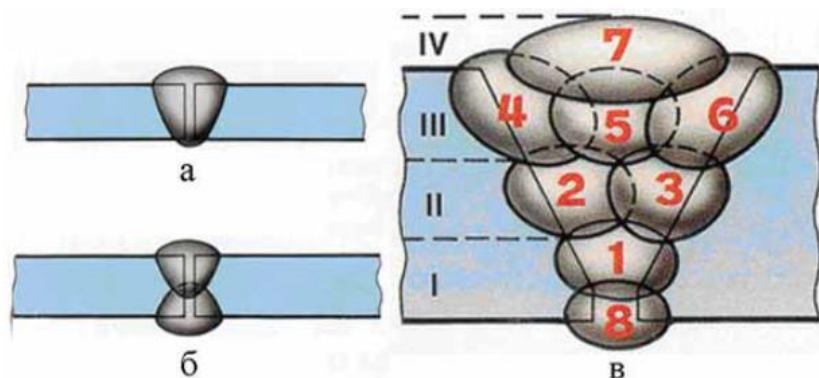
Одно-(а) и двухсторонний (б) односторонние швы и многослойный многопроходный сварной шов (в):1-8-очередность выполнения проходов;1-корневой шов; 7-облицовочный шов;8-подварочный шов; I-IVслои
